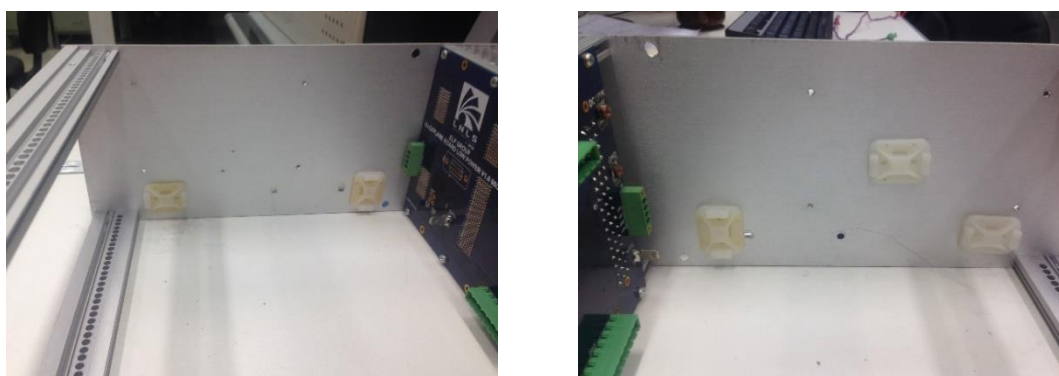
Inserção dos fixadores autoadesivos Reimold
